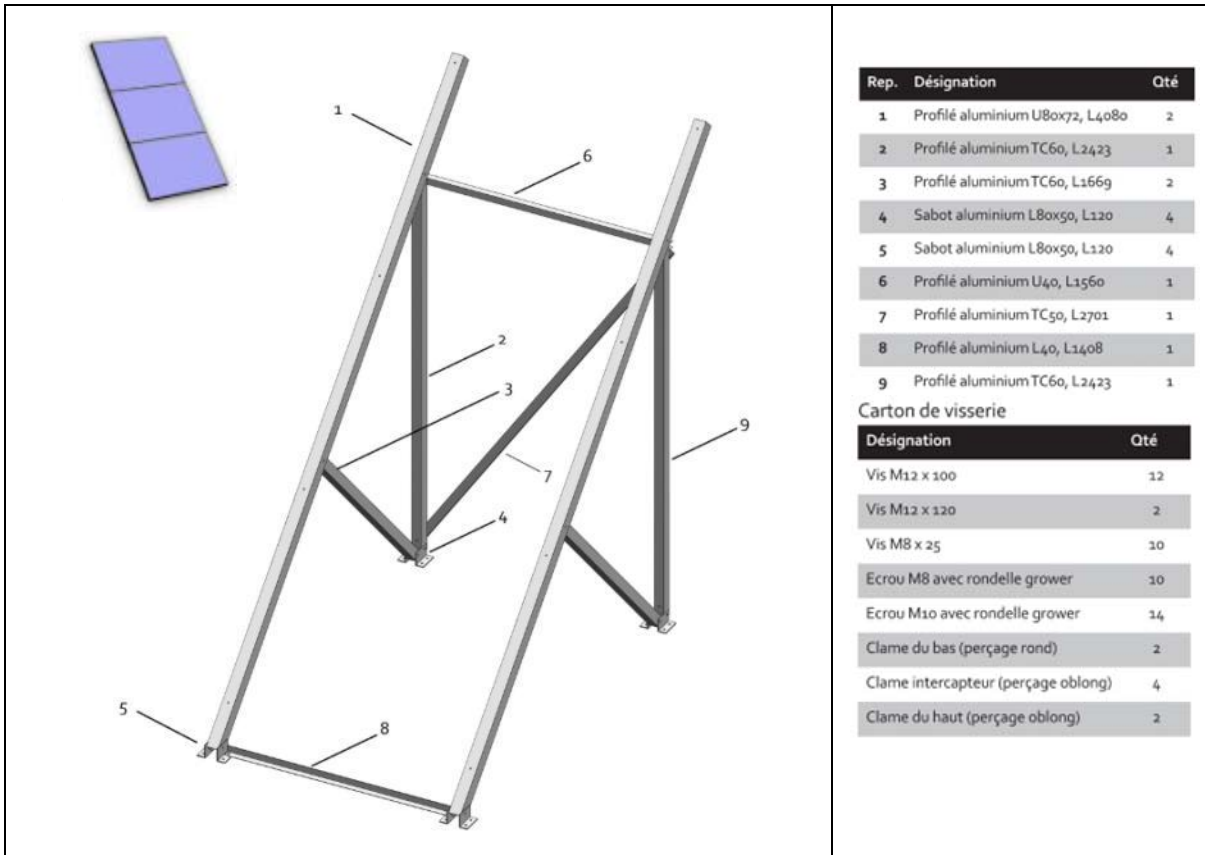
Kit de montage sur châssis pour 3 capteurs H232
